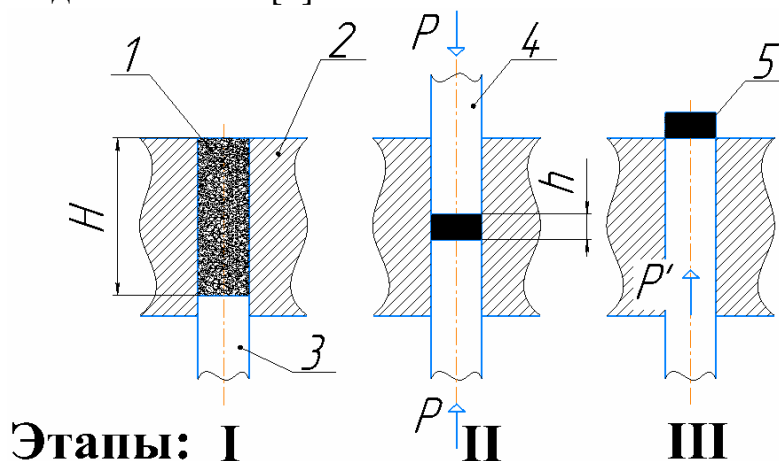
Иллюстрация процесса прессования в жесткой пресс-форме: 1 – твердосплавная смесь; 2 – матрица; 3 – нижний пуансон; 4 – верхний пуансон; 5 – компактированная заготовка
